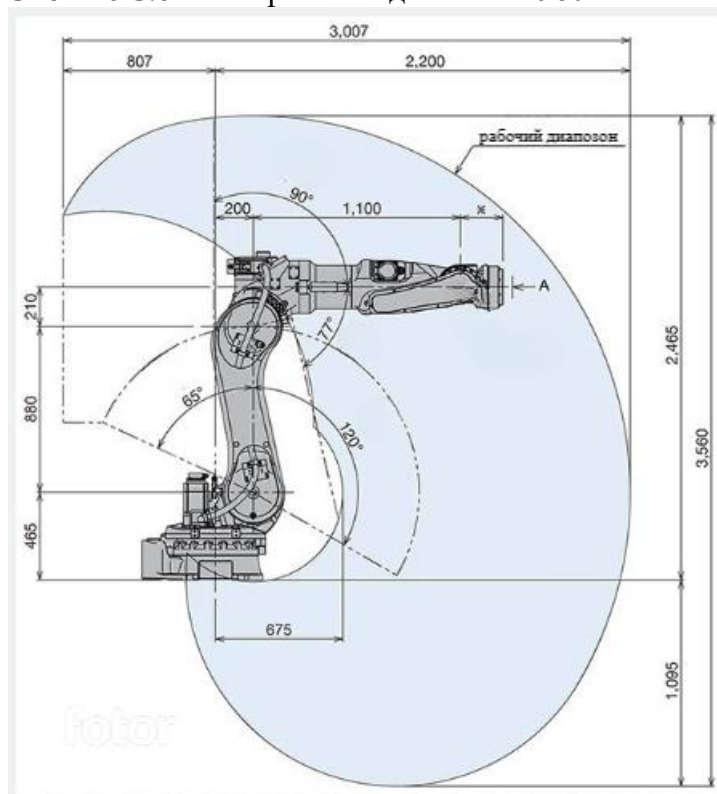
Размеры и диапазоны движения Kawasaki BX100N
